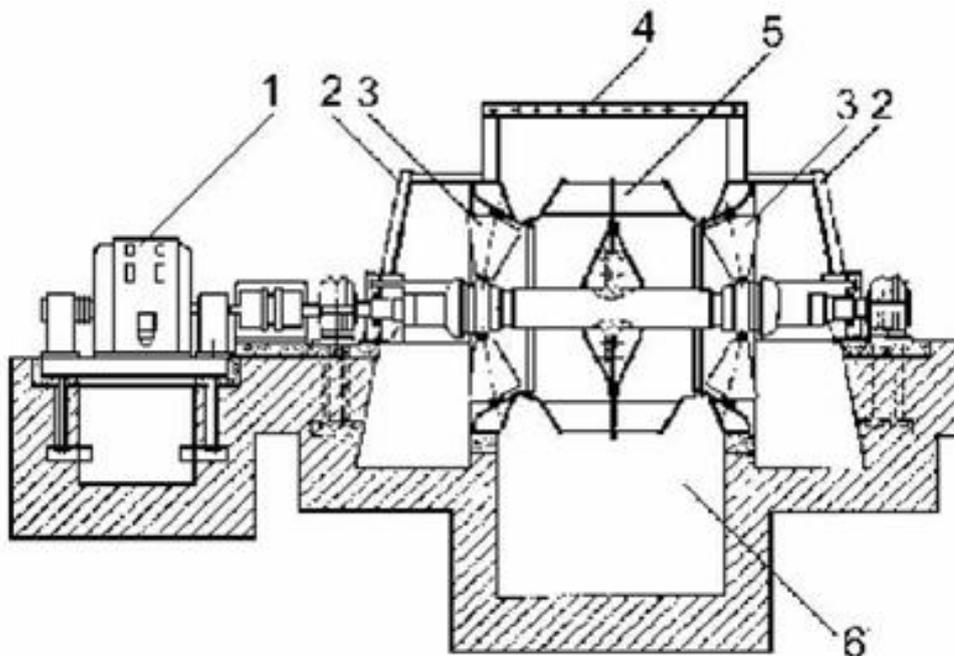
Центробежный вентилятор ВЦД-32: 1 - приводной двигатель; 2 - коробки всасывающих коллекторов; 3 - лопатки направляющих аппаратов; 4 - кожух вентилятора; 5 - рабочее колесо (сдвоенное); 6 - выходной канал
